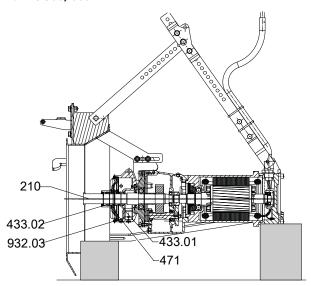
Montaje del cierre mecánico; Amaline 500, 600
